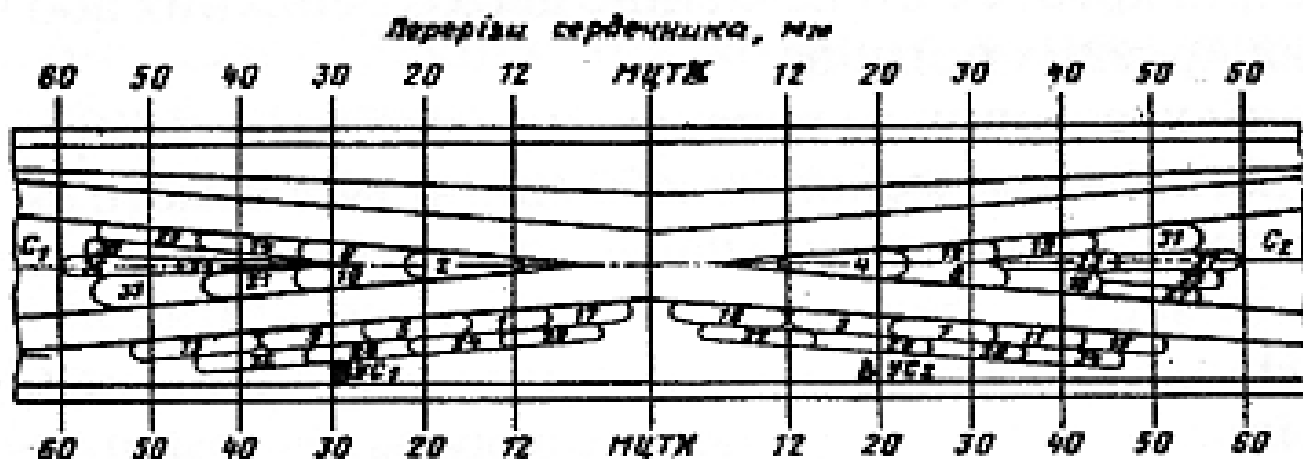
Схема расположения валиков наплавленного металла при ремонте тупых крестовин (1-38 – слой наплавки)
